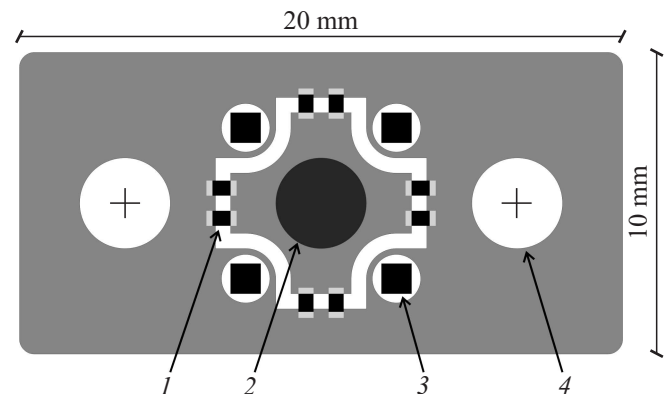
Эскиз печатной платы малоиндуктивного токоизмерительного шунта. Цифрами обозначены: 1 — резисторы 1Ω , 8 штук, типоразмер 0402; 2 — контактная площадка для SOS-образца, 3 — общие контакты коаксиального SMA-разъема, 4 — крепежные отверстия.
